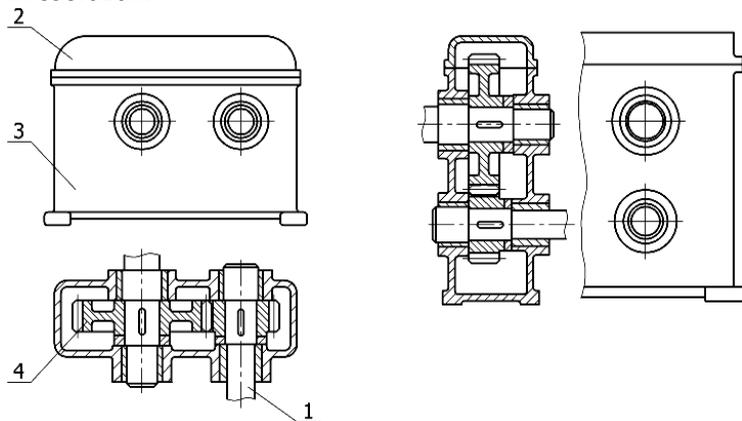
Конструкция одноступенчатого редуктора со
